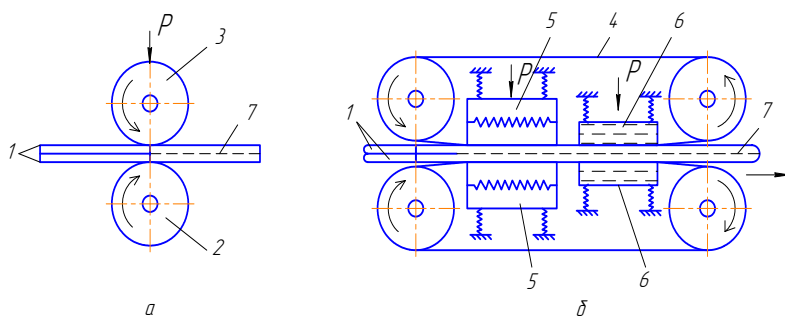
Схемы непрерывной сварки нагретым инструментом косвенным нагревом: а – роликовая сварка, б – ленточная двусторонняя сварка; 1 – свариваемые материалы; 2 – нагретый ролик; 3 – прижимной ролик; 4 – стальная лента; 5 – нагревательные губки; 6 – охлаждающие губки; 7 – сварной шов
